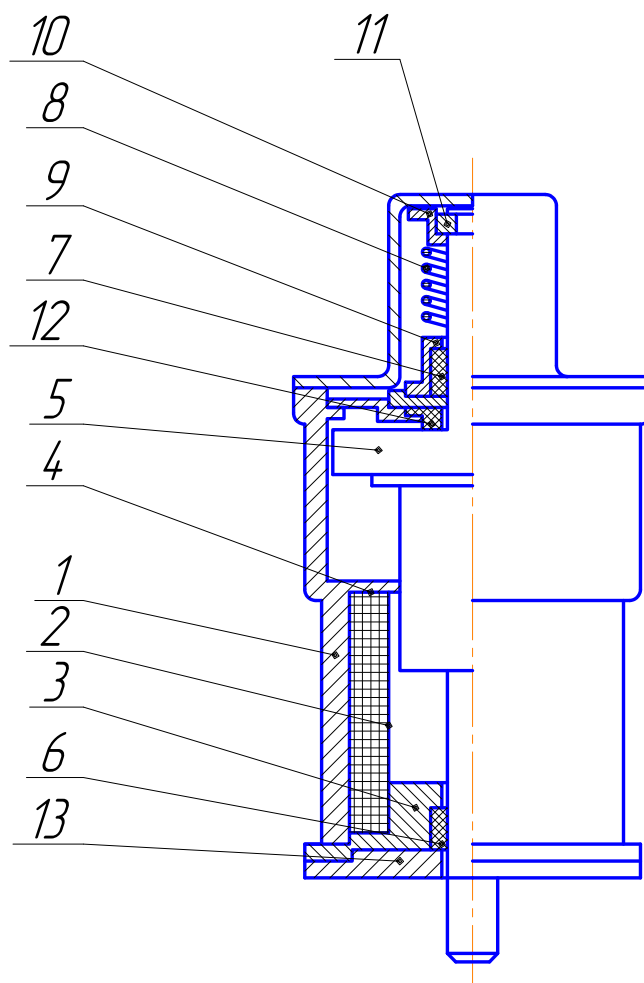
Конструкция ЛЭМД с двумя рабочими зазорами, комбинированным якорем и ферромагнитным направляющим корпусом
